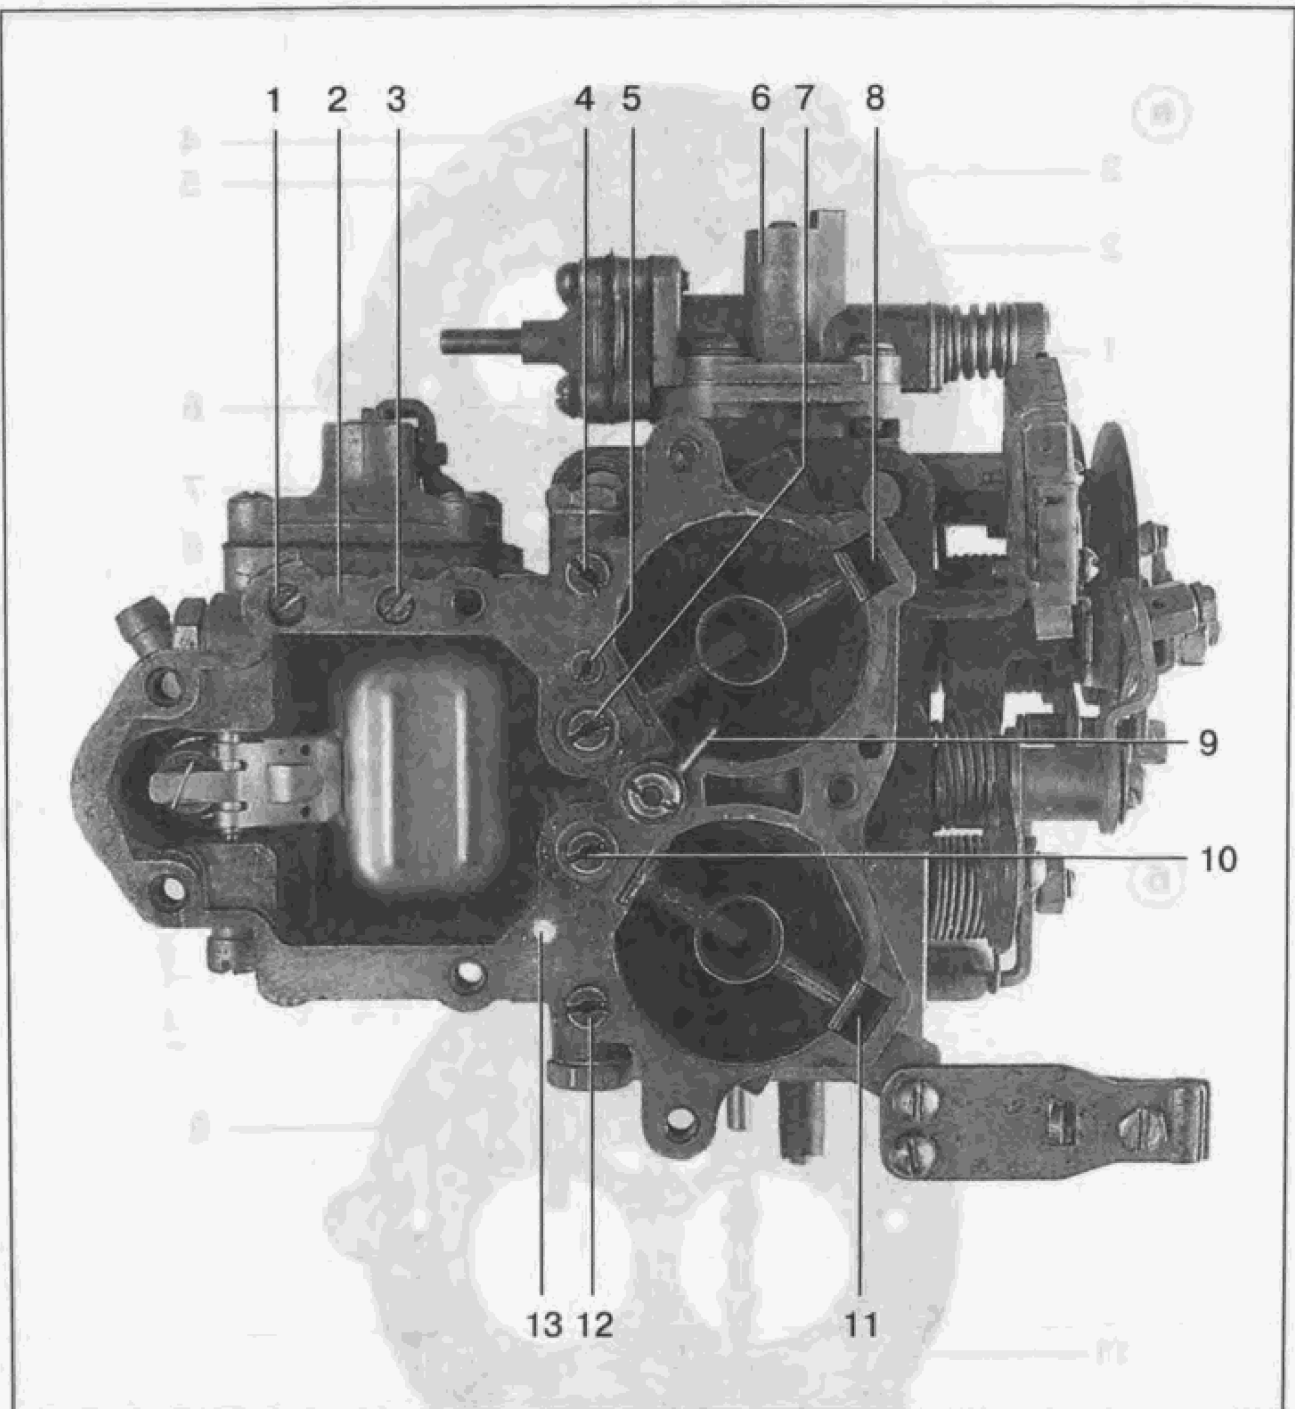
Вид на карбюратор со снятой крышкой сверху:
